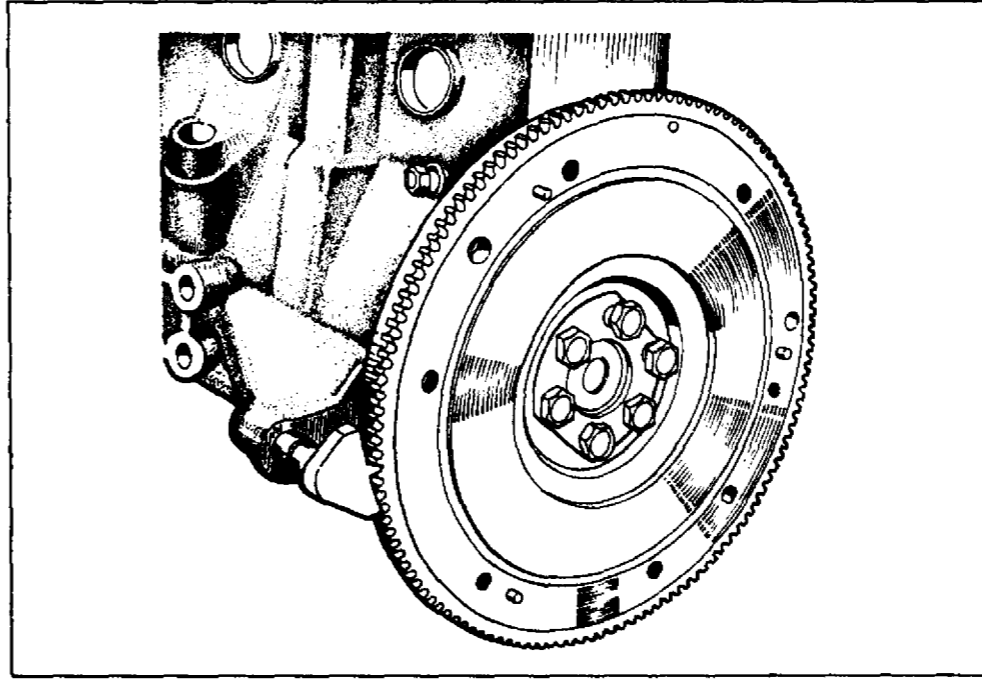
Блокировка маховика фиксатором 67.7820.9526
